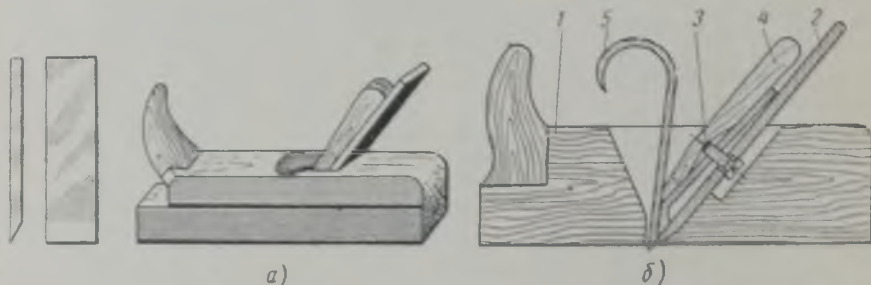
Одинарный (а) и двойной (б) рубанки:
